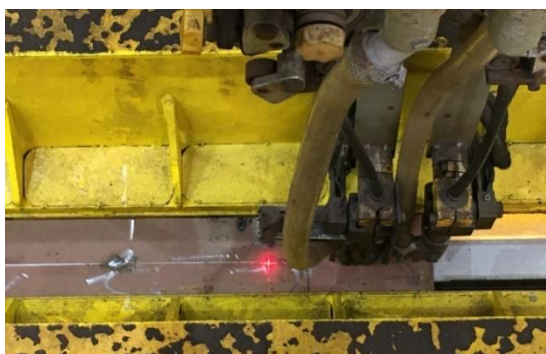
Posicionamento da tocha para dar início à soldadura
